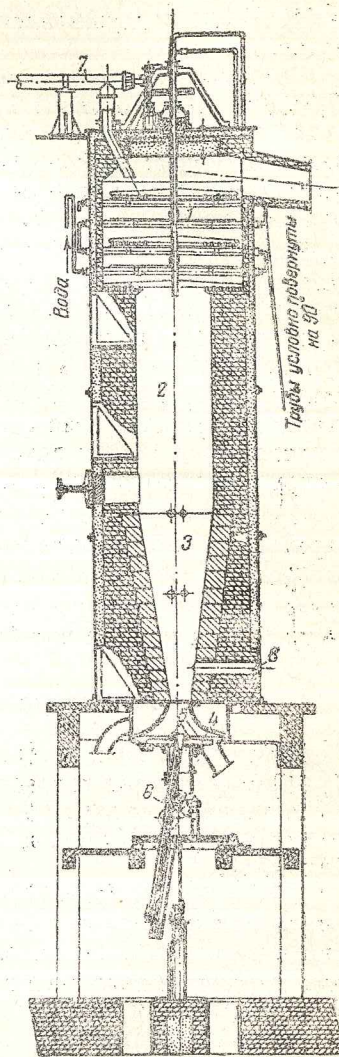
Газогенератор со взвешенным слоем: 1 — устройство для подсушки топлива; 2 — цилиндрическая часть шахты; 3 — конус; 4 — поддон; 5 — лопасти; 6 — штанга для очистки стенок шахты; 7 — шнек для подачи топлива; 8 — отверстие для возврата уноса.
